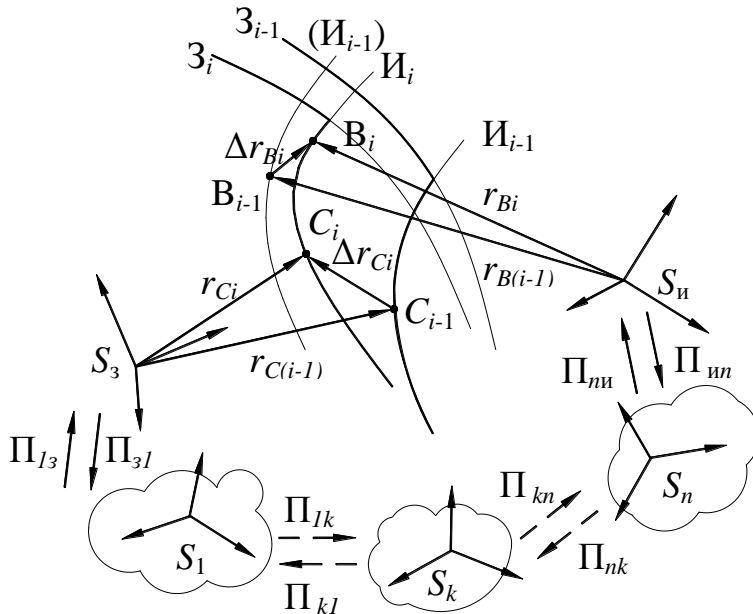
Обобщенная схема континуального взаимного формообразования заготовки и инструмента
